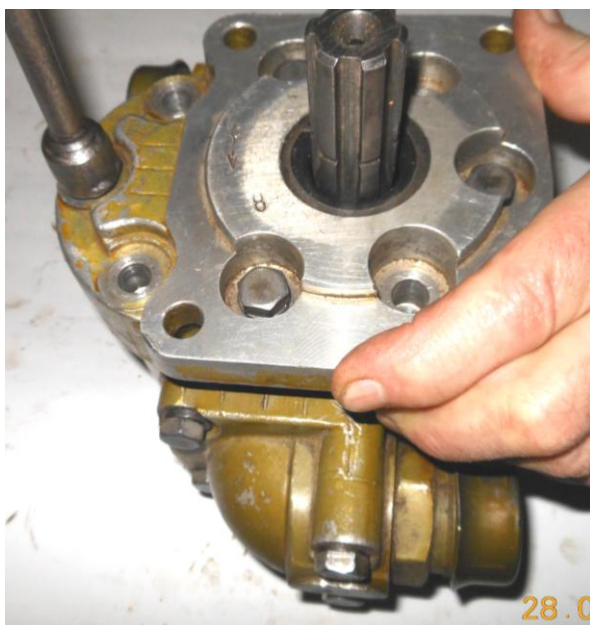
Обжатие болтов крепления крышки к корпусу насоса
